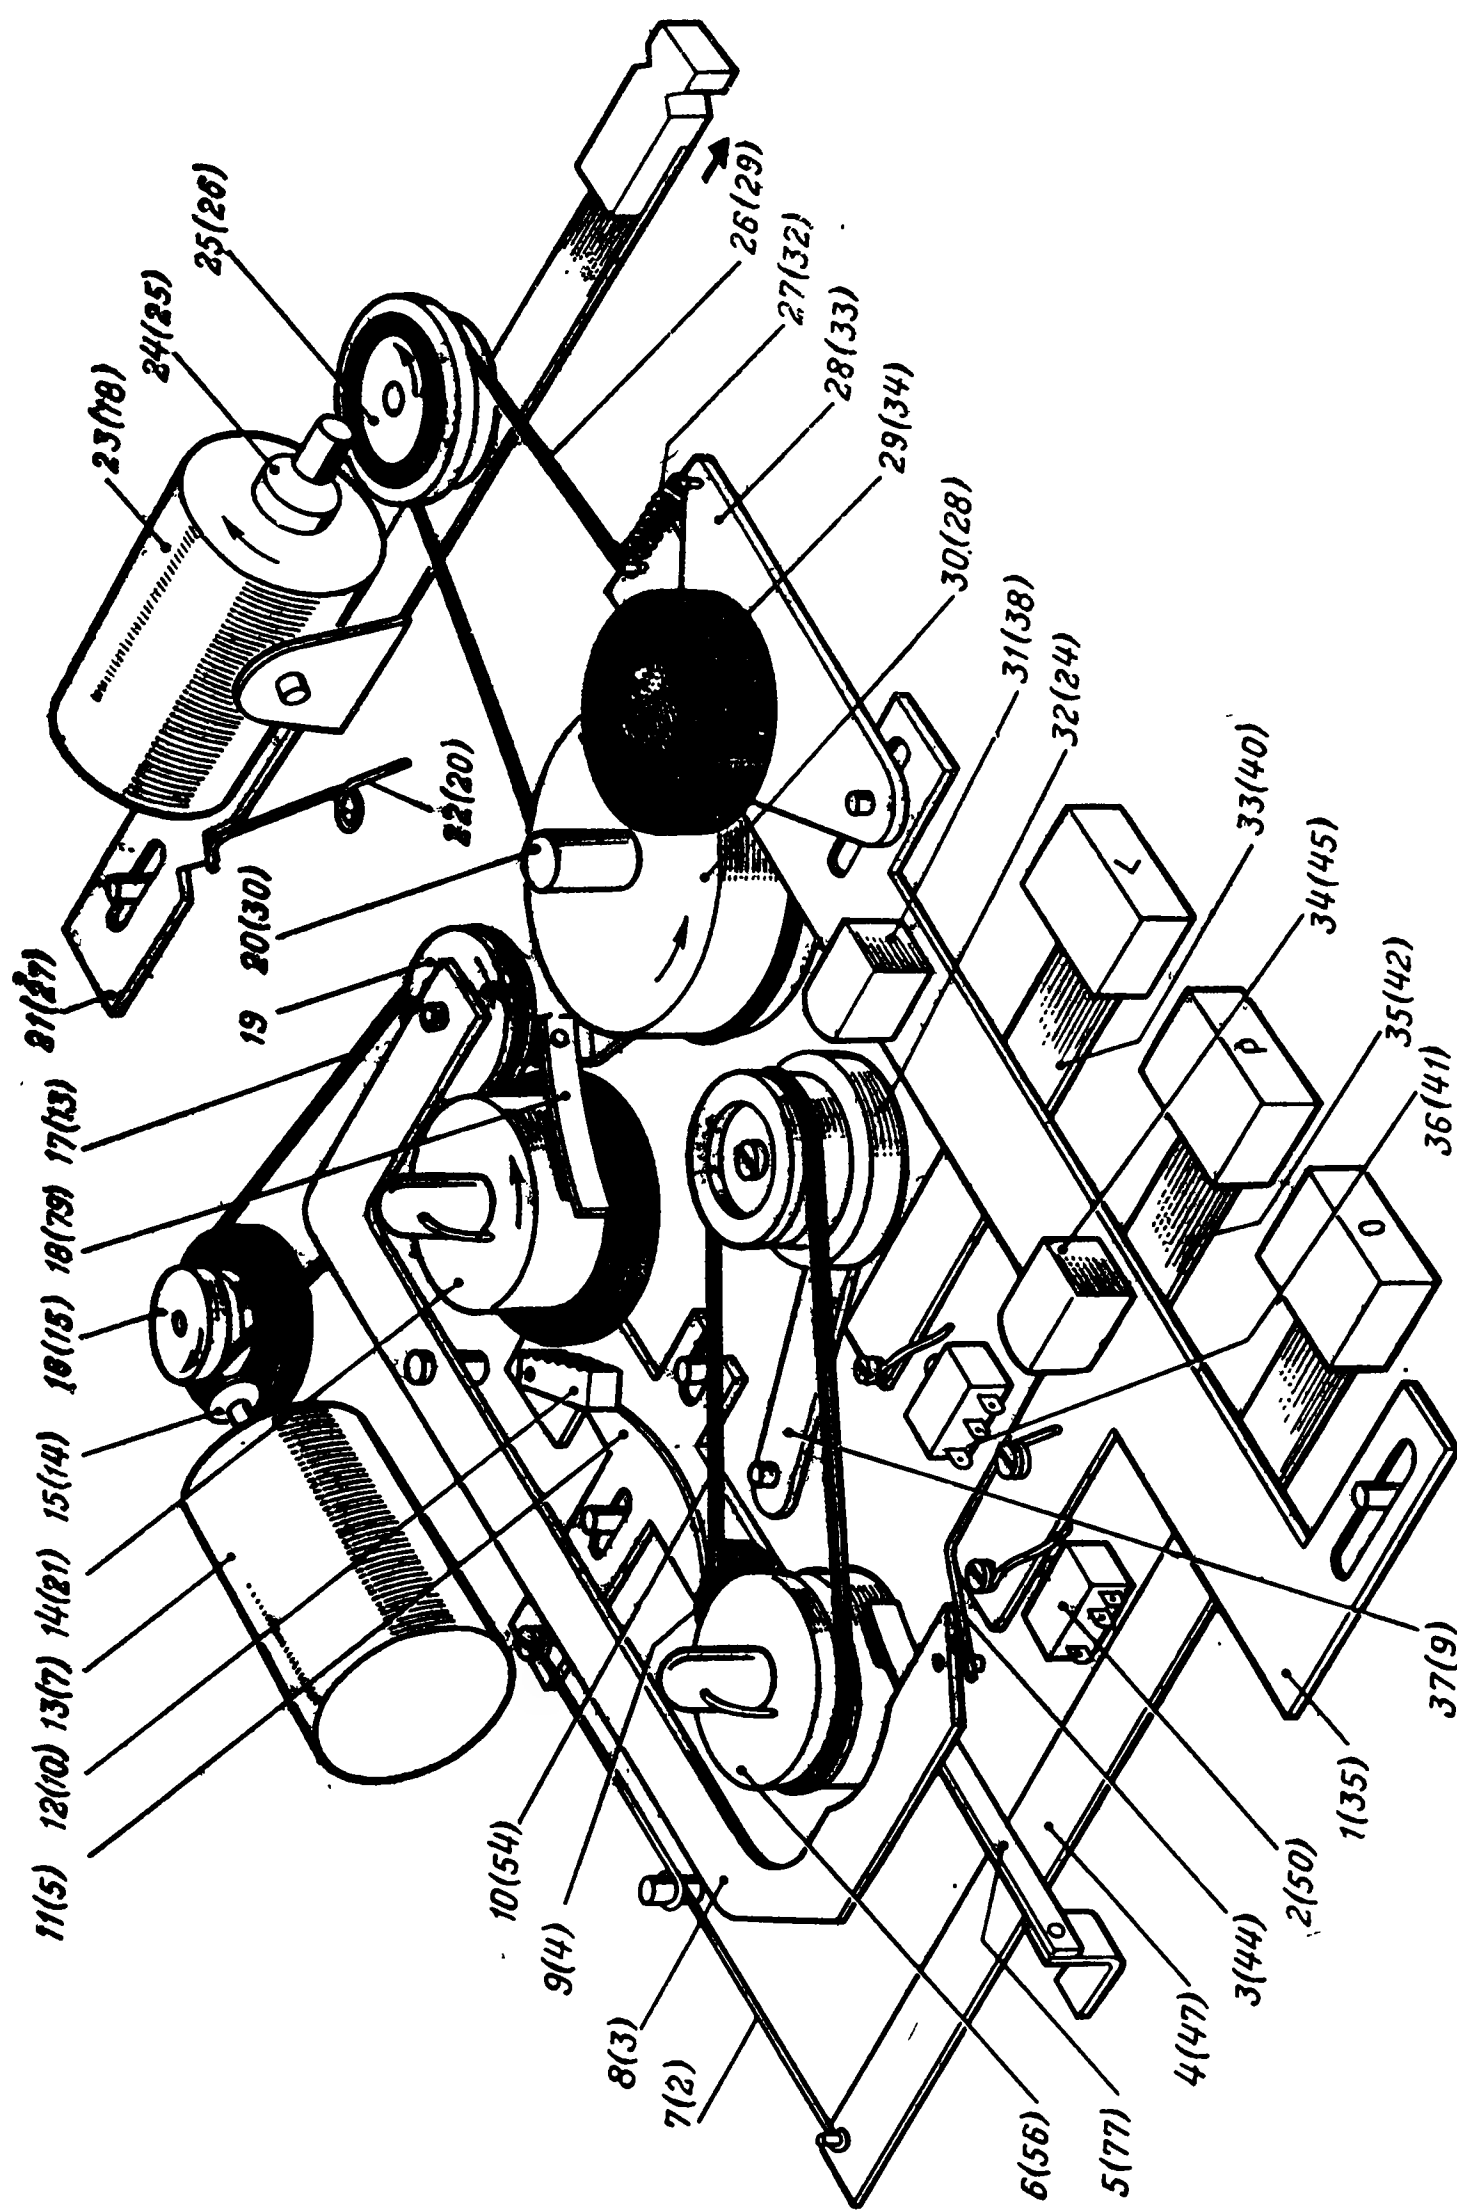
Кинематическая схема лентопротяжного механизма (в скобках даны номера деталей по сборочному чертежу лентопротяжного механизма)
